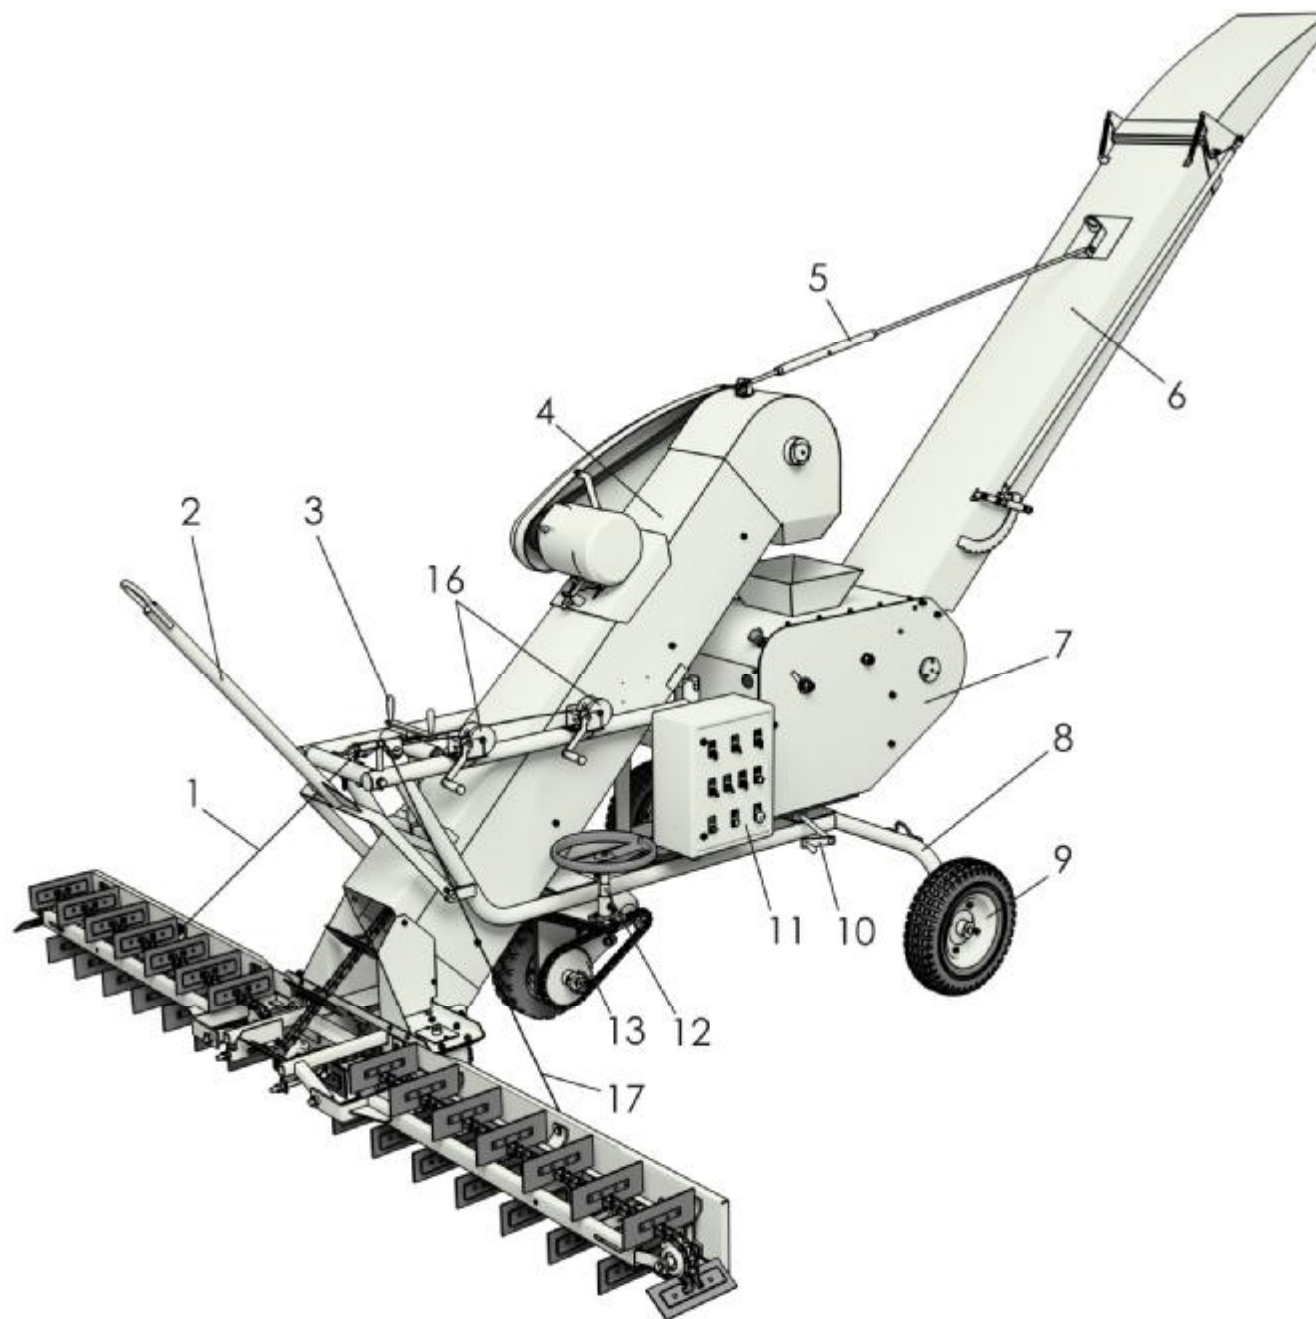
Основные сборочные единицы метателя зерна МЗС-90-20-01М
